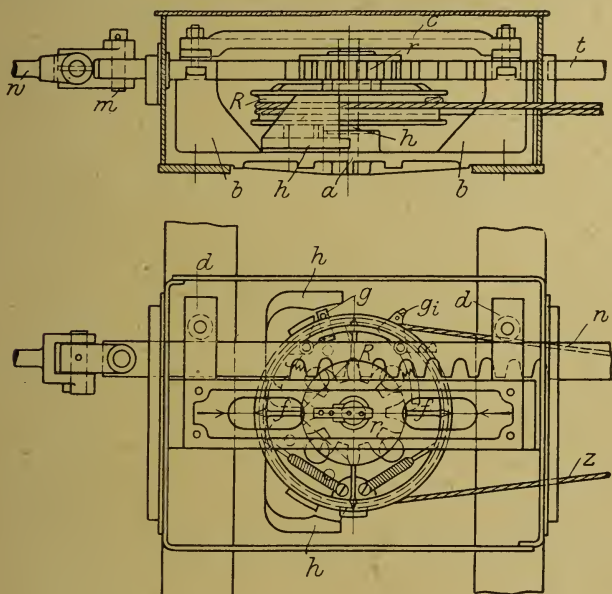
Weichenbetrieb mit Drahtbruchsperr.
